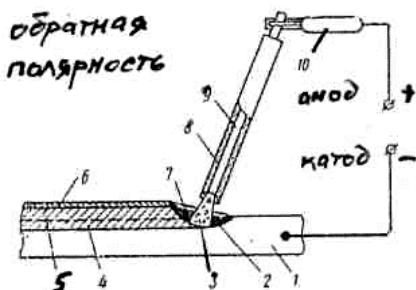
Ручная дуговая сварка штучным электродом: 1 – основной металл; 2 – сварочная ванна; 3 – электрическая дуга; 4 – проплавленный металл; 5 – наплавленный металл; 6 – шлаковая корка; 7 – жидкий шлак; 8 – электродное покрытие; 9 – металлический стержень электрода
